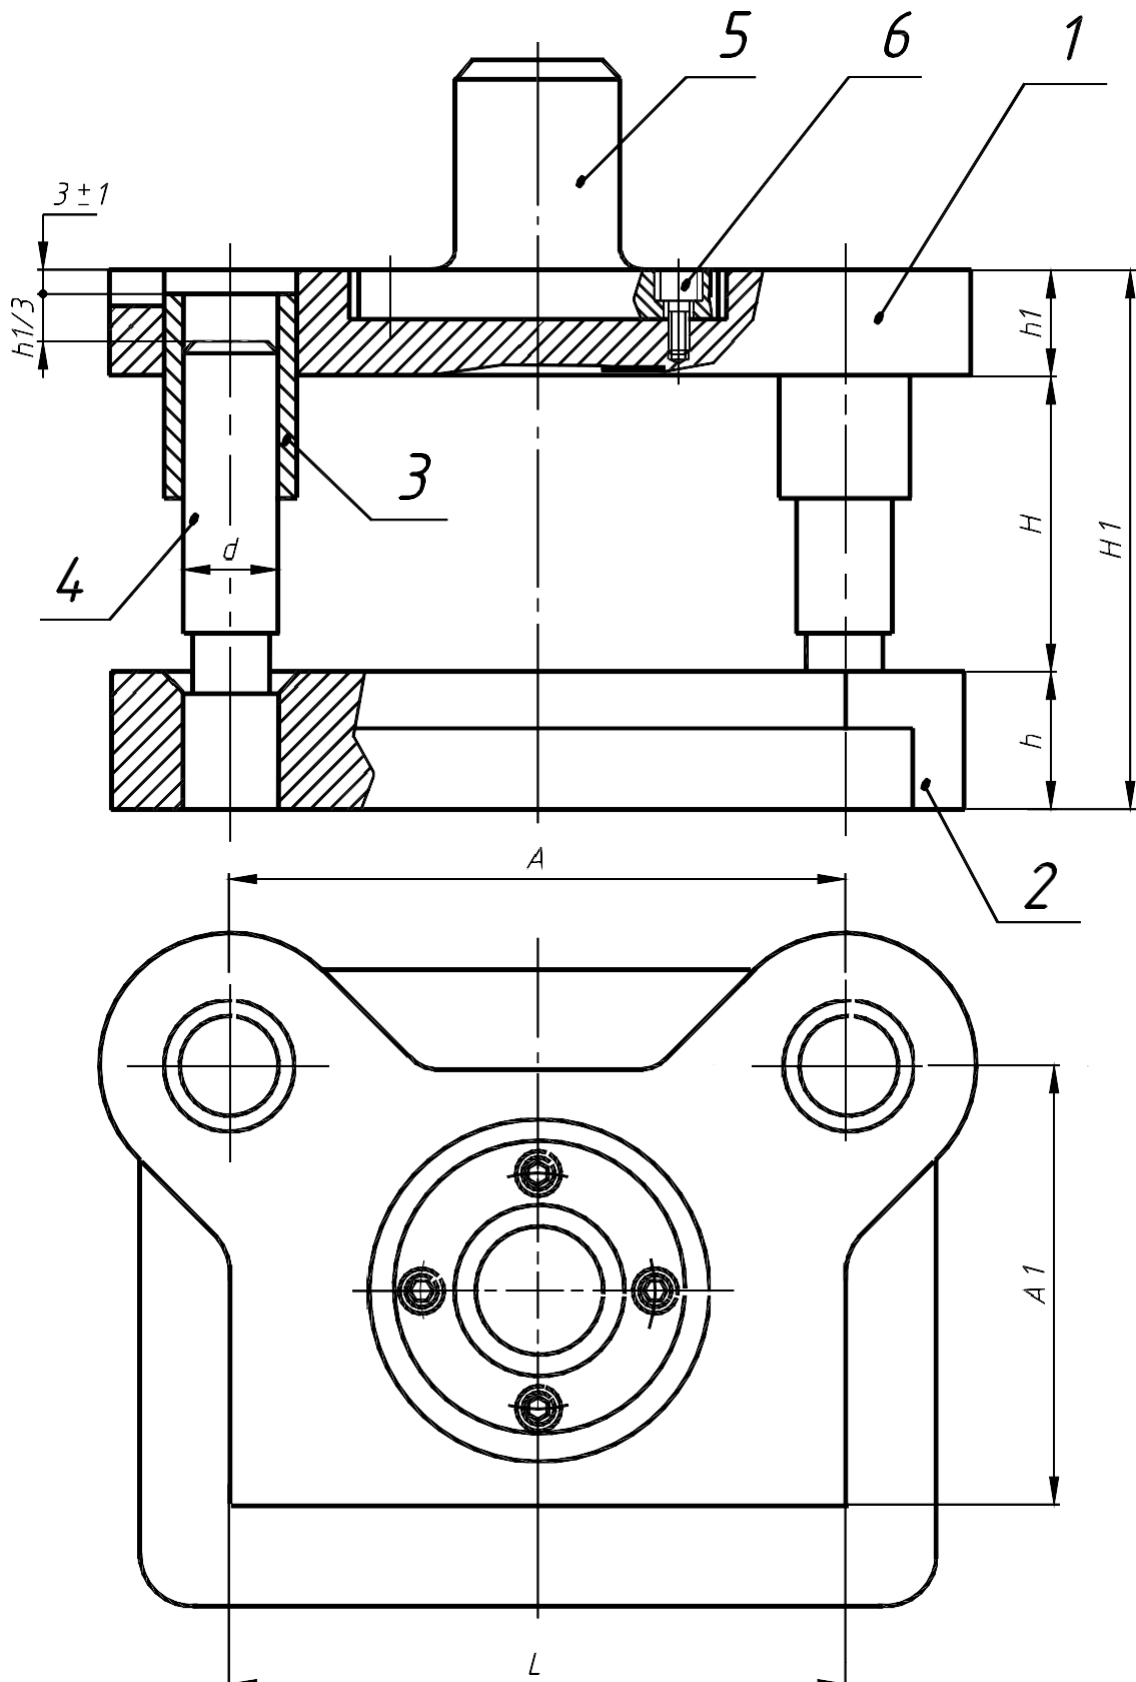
Фрагмент сборочного чертежа блока штампа. 1 - плита верхняя, 2 - плита нижняя, 3 - втулка; 4 - колонка; 5 - хвостовик; 6 - винт.
